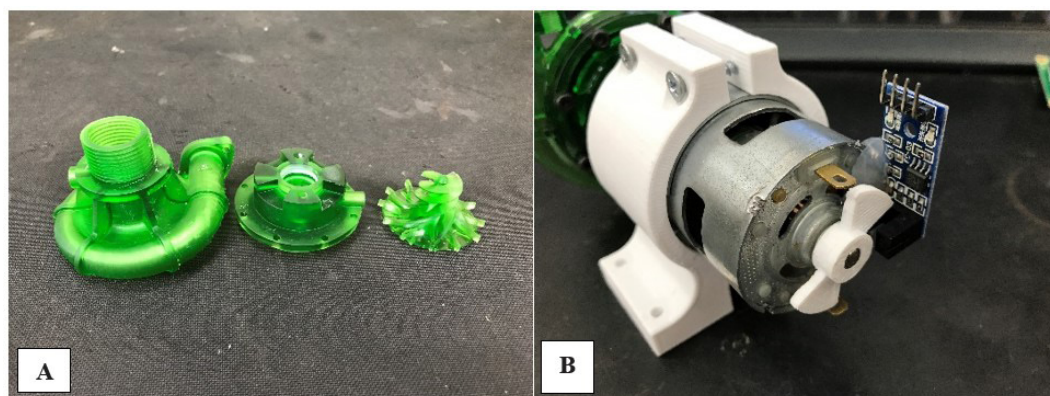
Componentes feitos em impressora SLS e Tacômetro óptico instalado no eixo da bomba.
